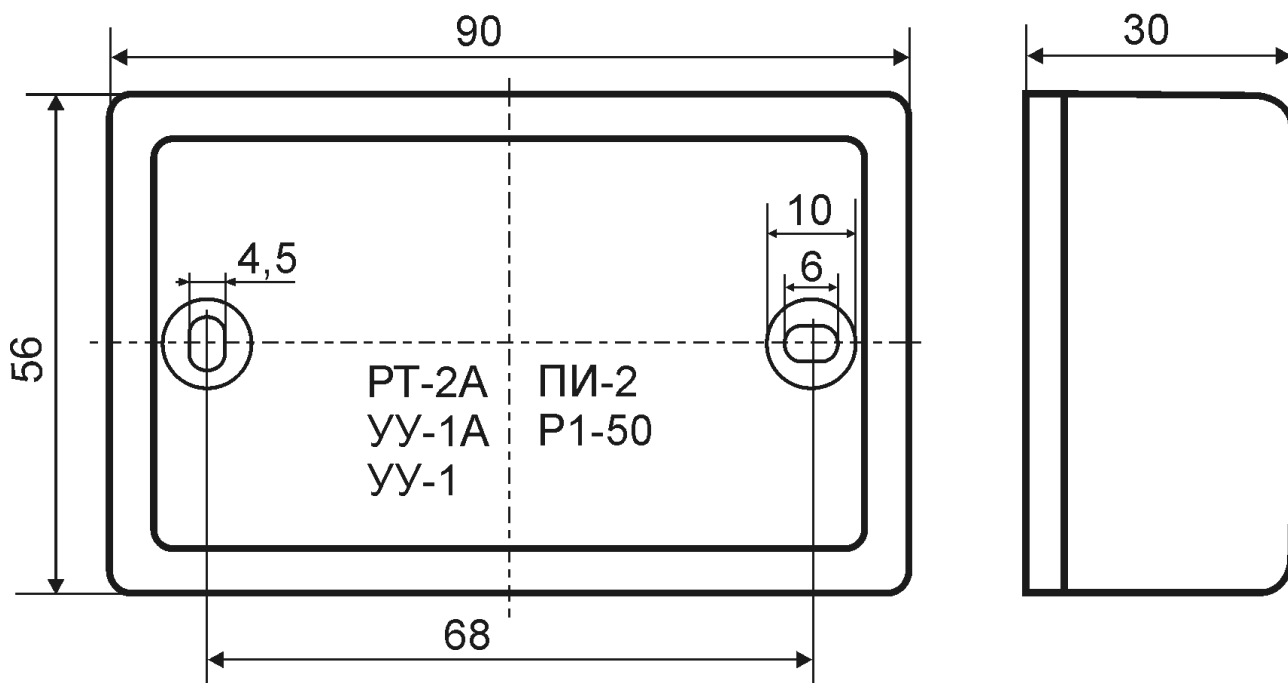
Габаритные и установочные размеры РТ-2А, УУ-1, УУ-1А, Р1-50, ПИ-2
